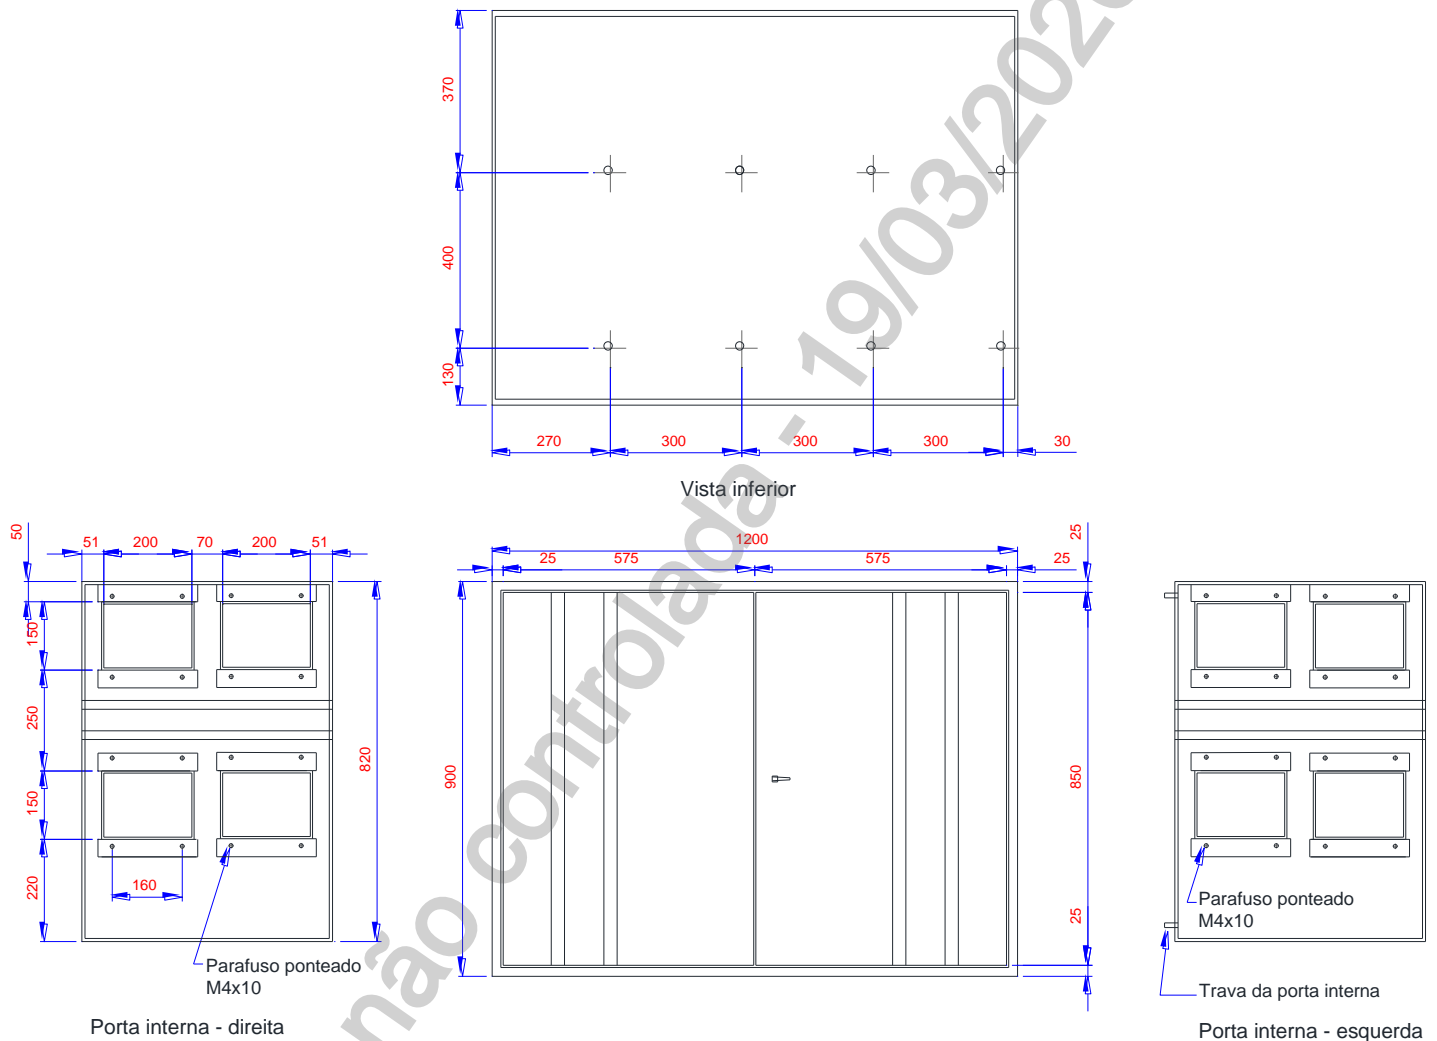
Caixa Metálica para Medição Indireta Tipo M – 1/2
